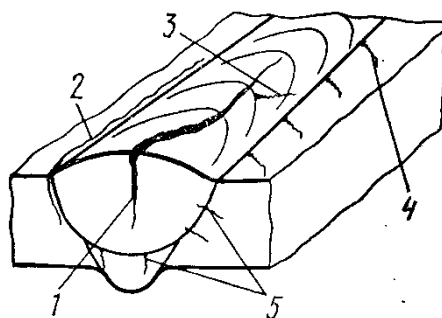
Гарячі тріщини у зварних з'єднаннях:
